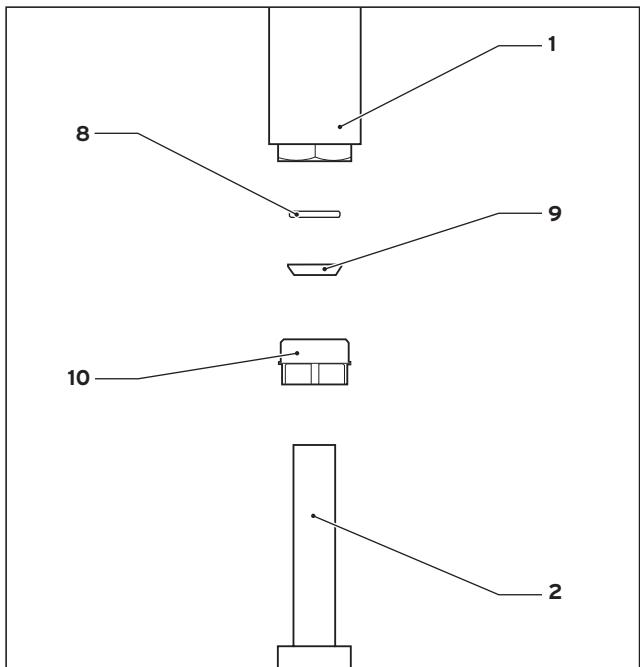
Montage du dispositif de serrage dans le tuyau de retour
